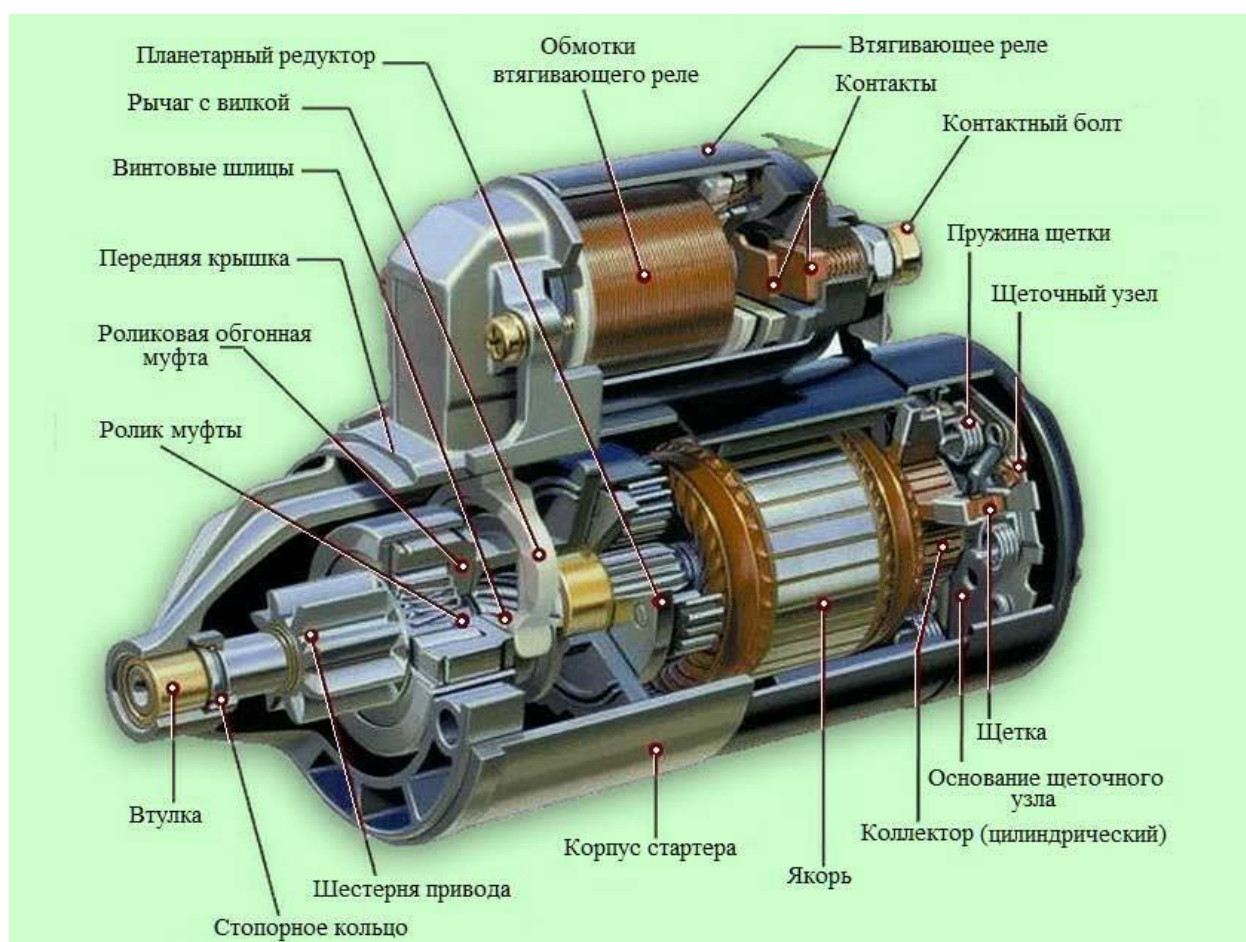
Общее устройство стартера с планетарным редуктором
